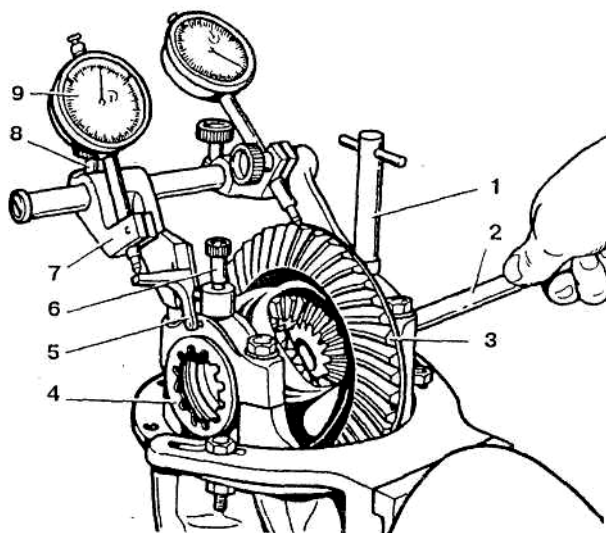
Проверка предварительного натяга подшипников коробки дифференциала приспособлением А.95688/R:
